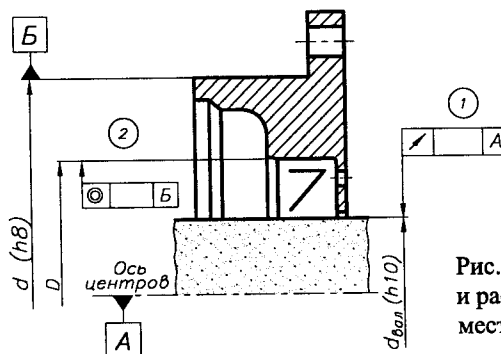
Допуски формы и расположения поверхностей места установки манжеты
